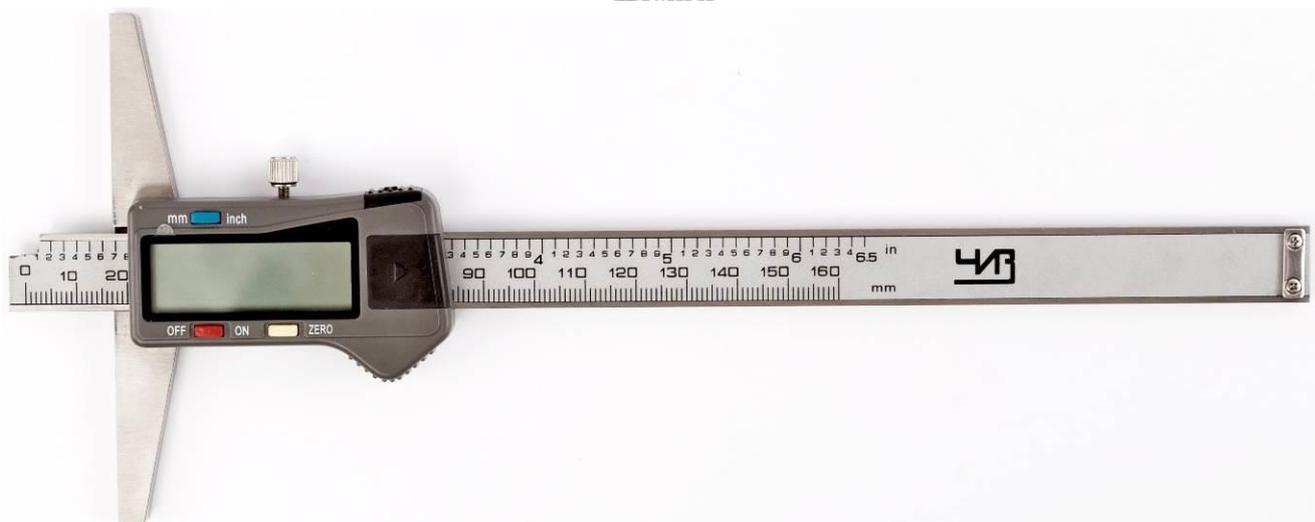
Общий вид штангенглубиномеров модификации ШГЦ со ступенчатым торцом штанги
